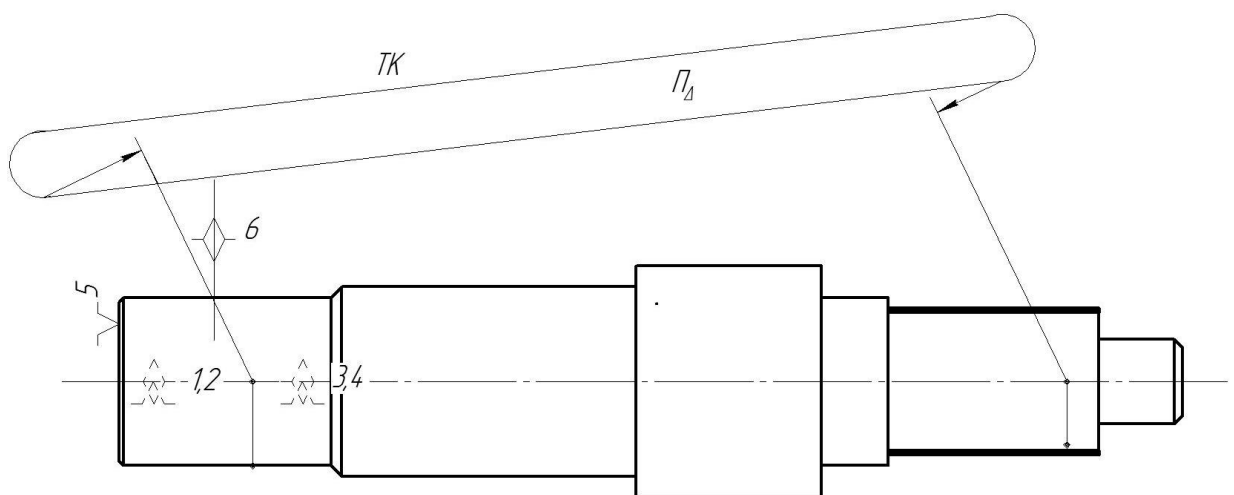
Базування вала (перший варіант) при обробці поверхні під шестерню
